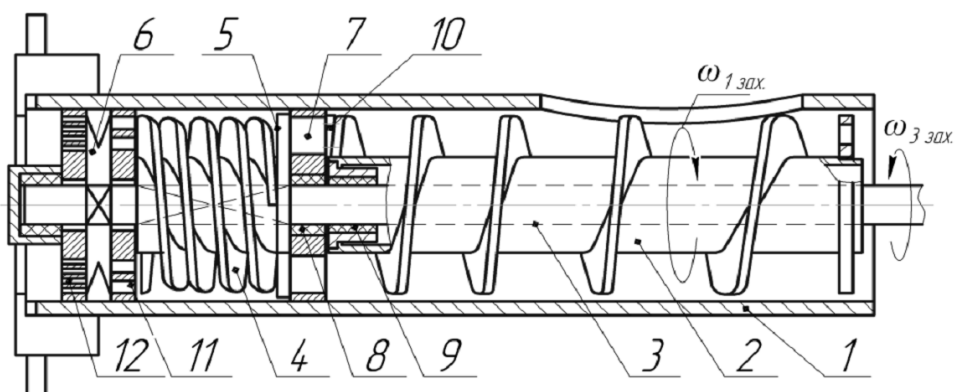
Структурна здрібнювально-подаючого механізму: 1 – корпус; 2 – гвинт подаючий; 3 – приводний вал; 4 – гвинт багатозахідний; 5 – ніж першого здрібнення; 6 – ніж другого здрібнення; 7 – пластина з отворами; 8, 9 – підшипники; 10 – кінець витка гвинта; 11, 12 – пластина проміжна та кінцева.
